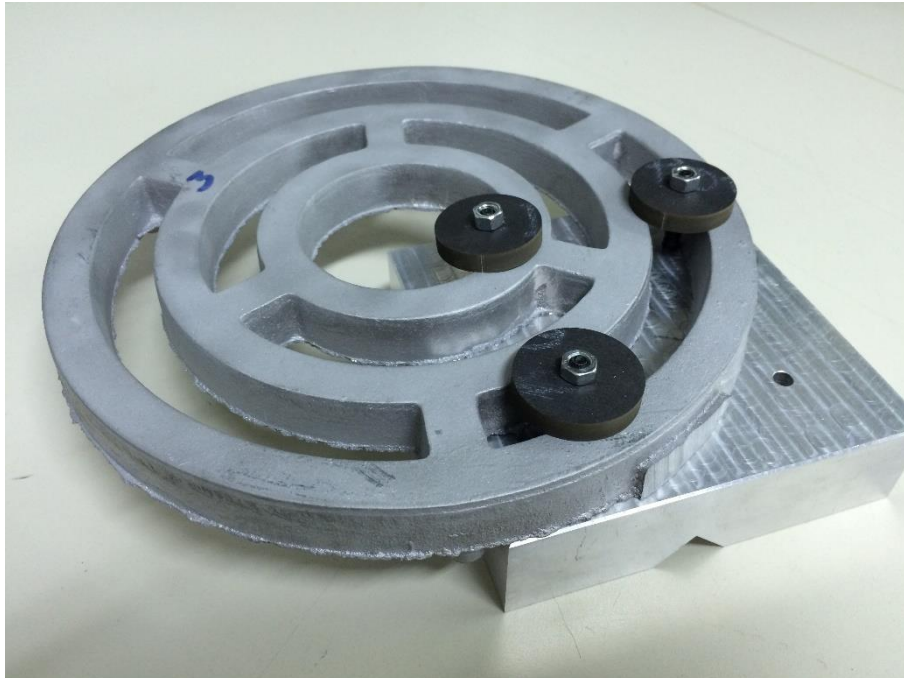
Peça 3 de fundição fixa à parte móvel do Gabari.
